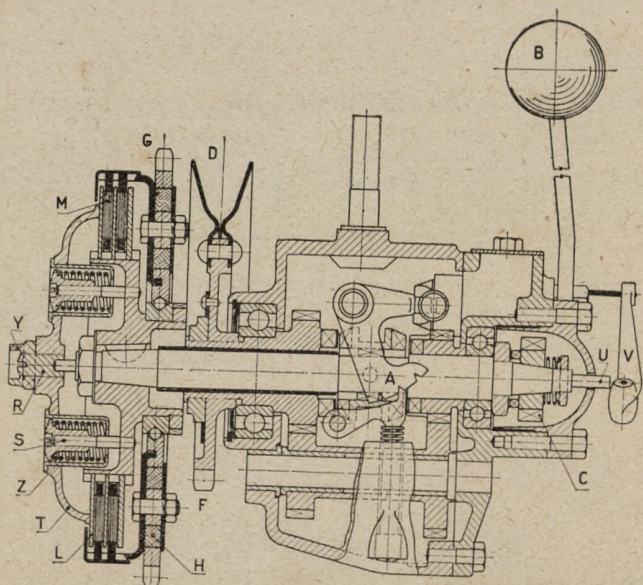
a. Hlavní hřídel s příčným spojkovým klínem.
